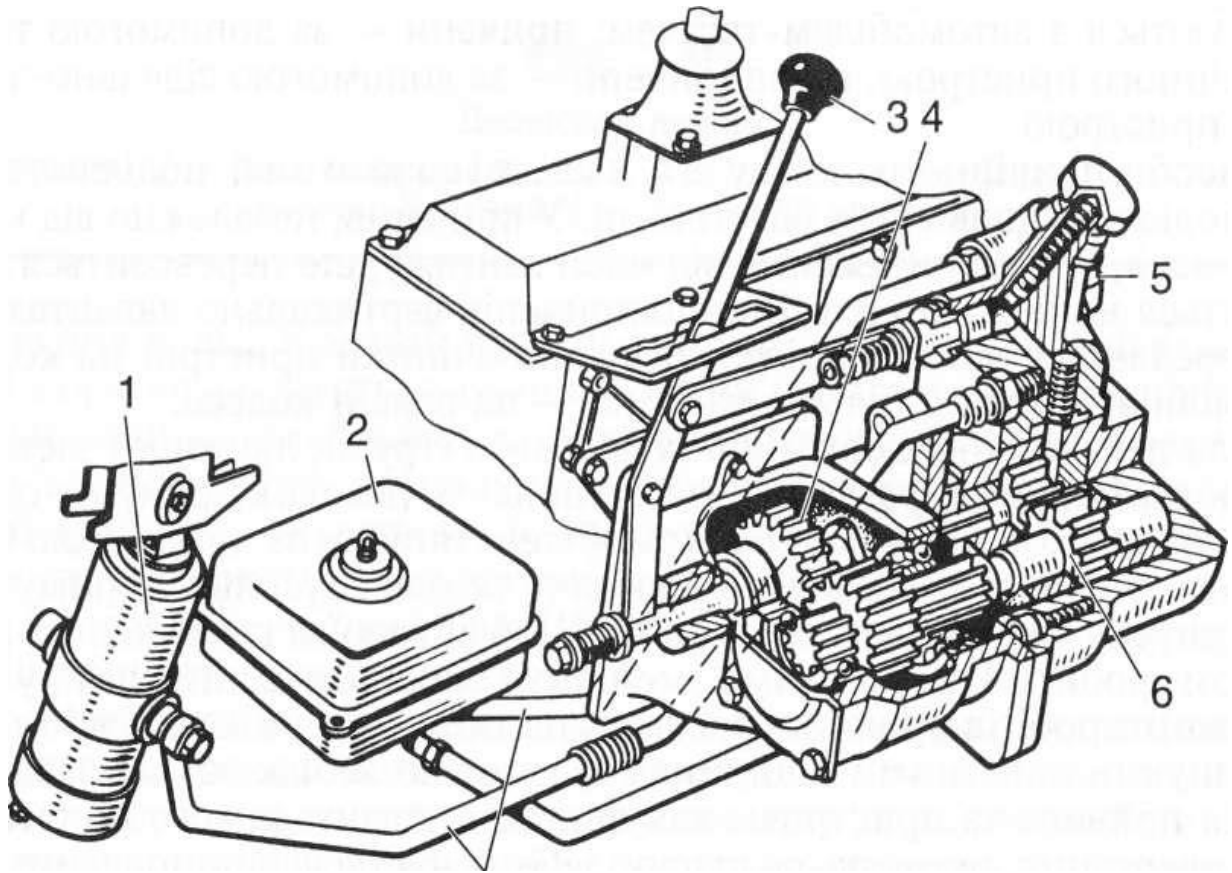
Гідравлічний підйомний механізм: 1 — циліндр; 2 — бак для робочої рідини; 3 — важіль; 4 — коробка відбирання потужності; 5 — кран керування; 6 — шестеренчастий оливний насос; 7 — трубопроводи.
